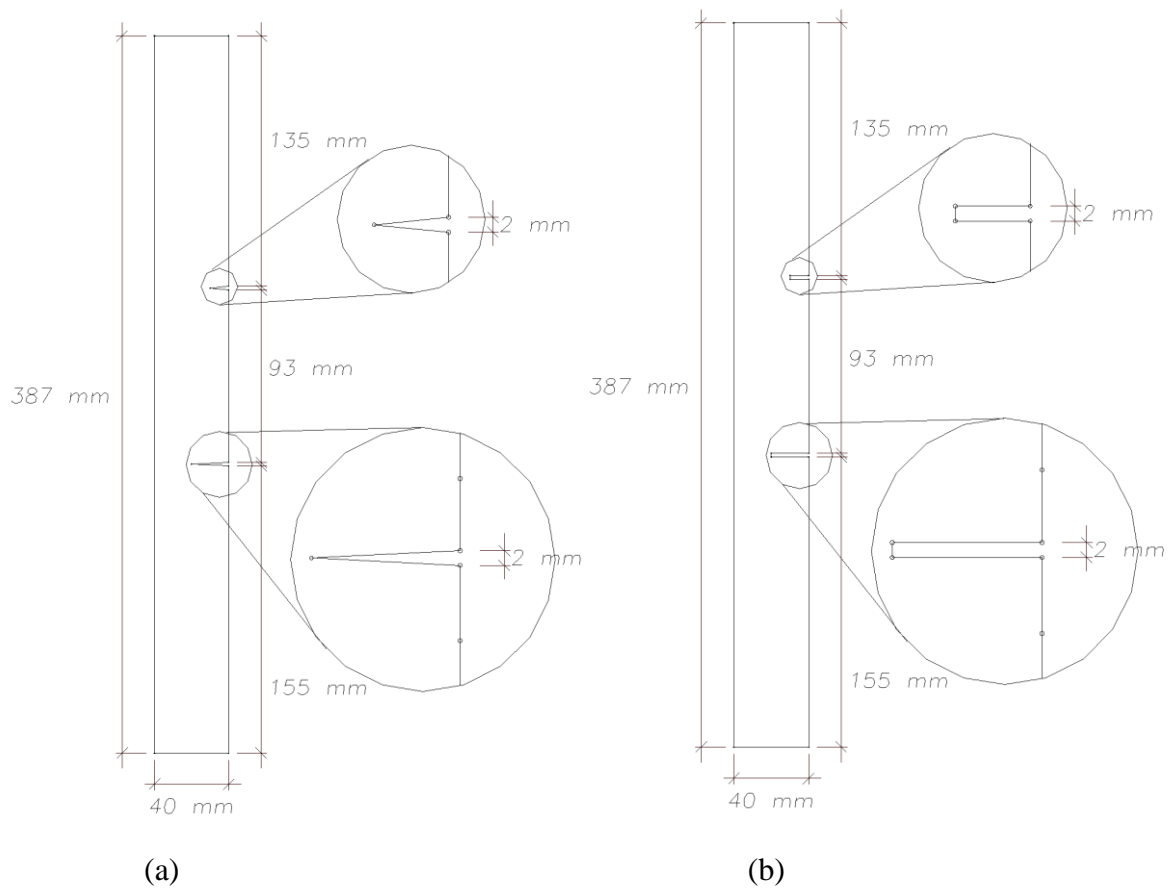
Modelo da placa: (a) com fissura angular; (b) com fissura retangular.
